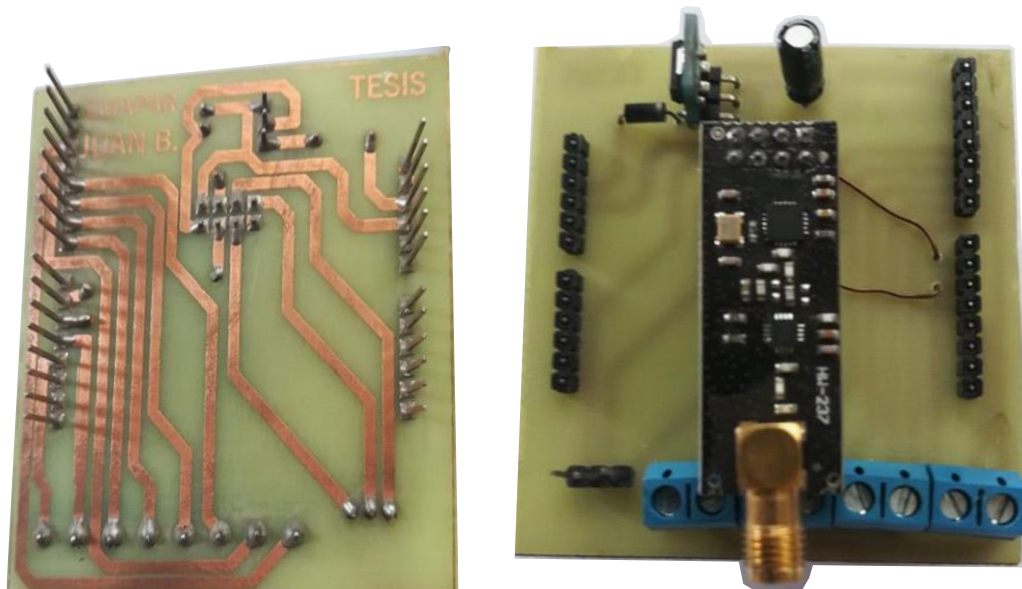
Placa inalámbrica nodo servidor soldado
